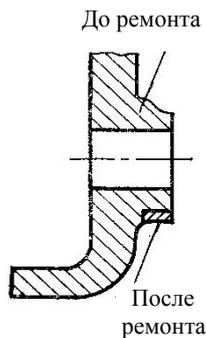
Схема установки бандажей для восстановления обломанной бобышки корпусной детали
